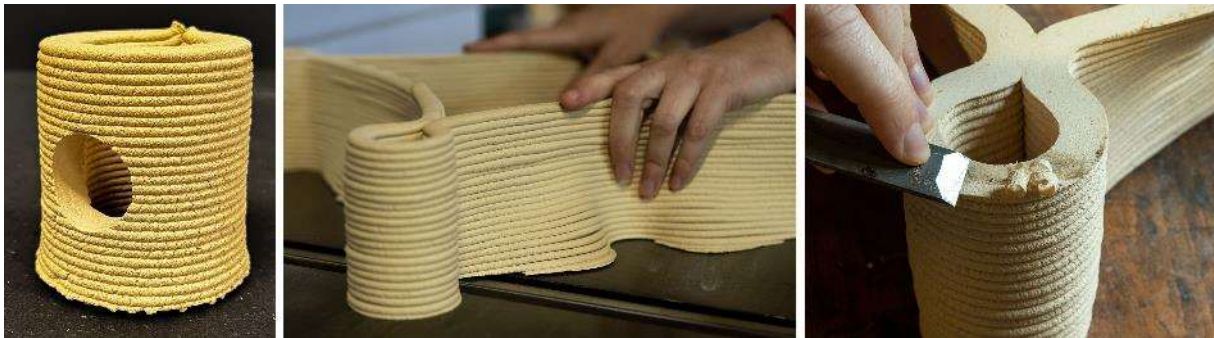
Untersuchung verschiedener Holzbearbeitungsmethoden – Bohren, Hobeln, Schnitzen
